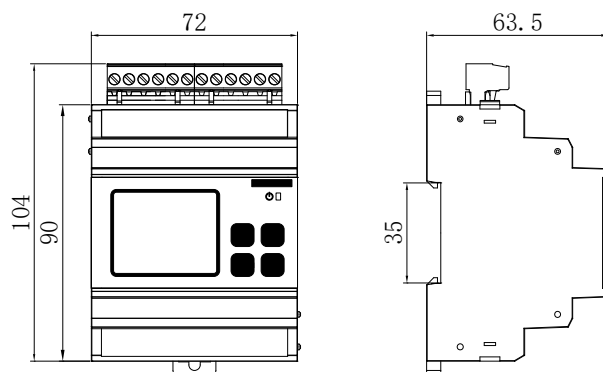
Внешний вид и габаритные размеры приборов
